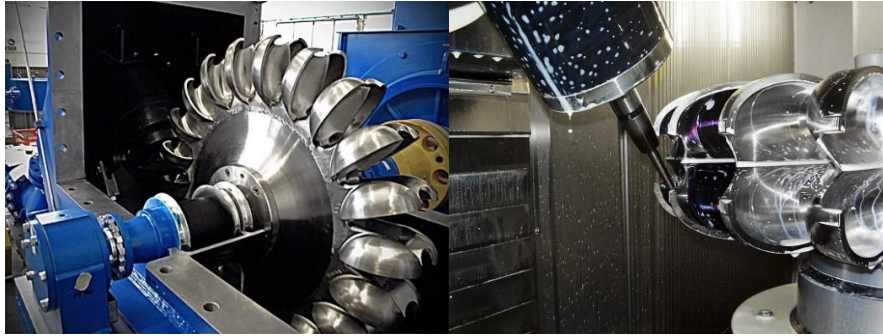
Turbina Pelton. Fuente: directindustry.es
